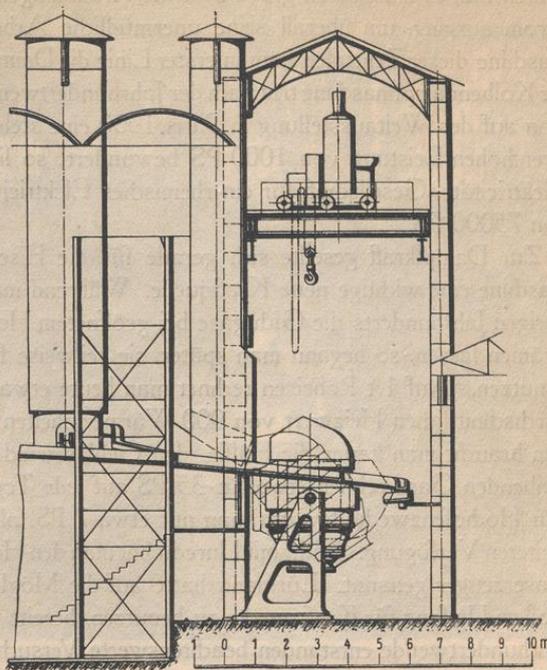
Mit Dampf betriebener Laufkran im Stahlwerk Hayingen. Nach einer Zeichnung aus dem Jahre 1879 aus dem Nachlaß von Alfred Trappen.
